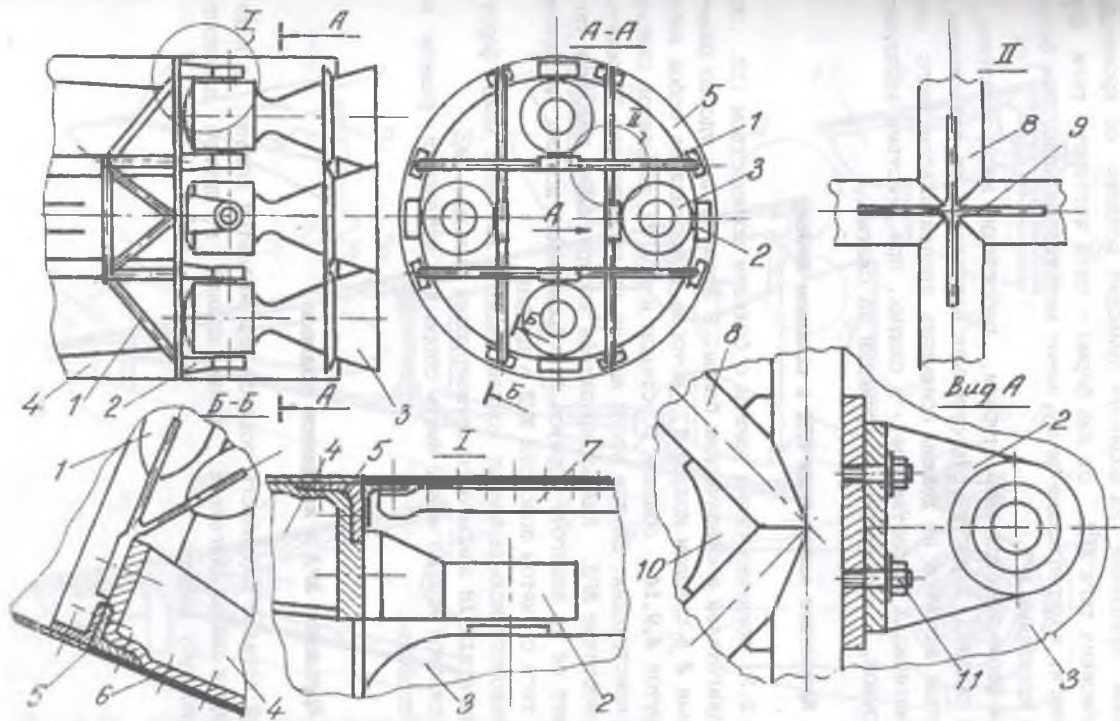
Ферменное крепление поворотных ЖРД:
